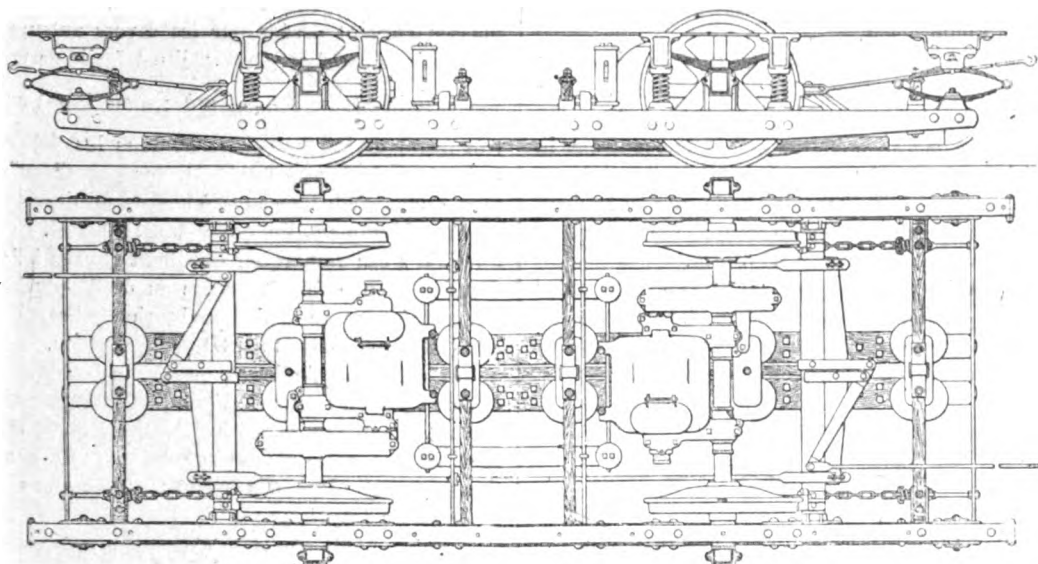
Plan et élévation du truck de la voiture du système Brown.
